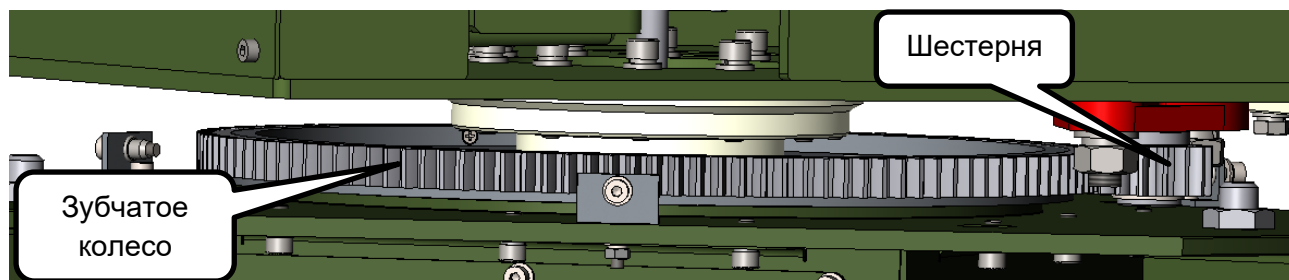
Внешний вид зубчатого колеса и шестерни азимутального привода СССТ 1,2 м (защитная лента не показана).
